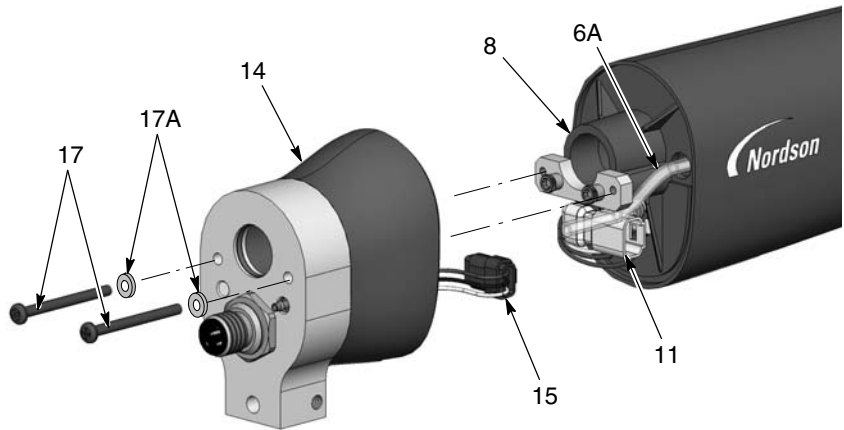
Desmontagem de pistola com barra de suporte 1 de 3
